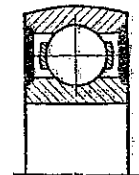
Шарикоподшипник со сферической поверхностью наружного кольца
